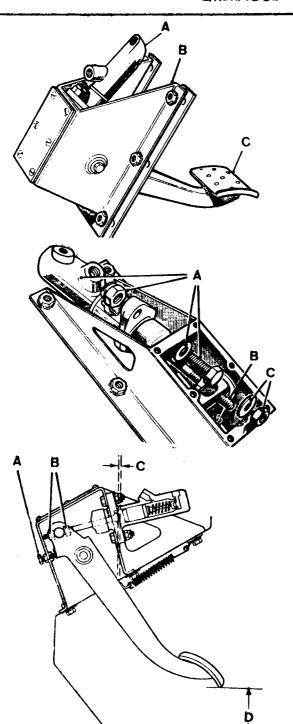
Conjunto del soporte, pedal y cilindro principal.
